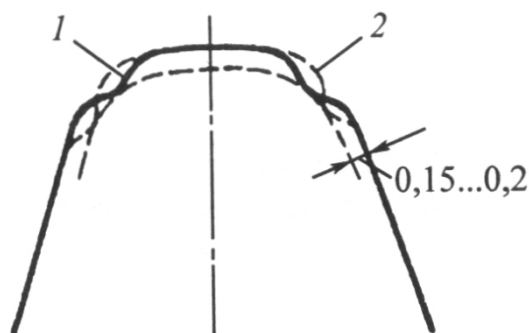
Прогрессивная схема со стружкоразделительными полукруглыми канавками на вершине зуба
